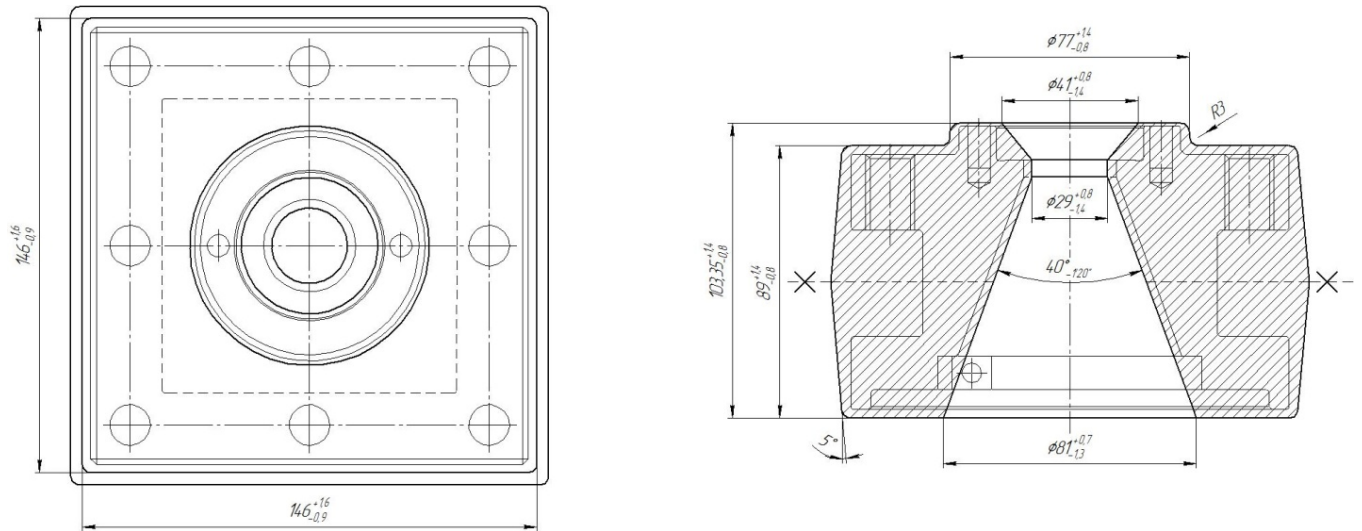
Креслення заготовки деталі (поковка на ГKM)
